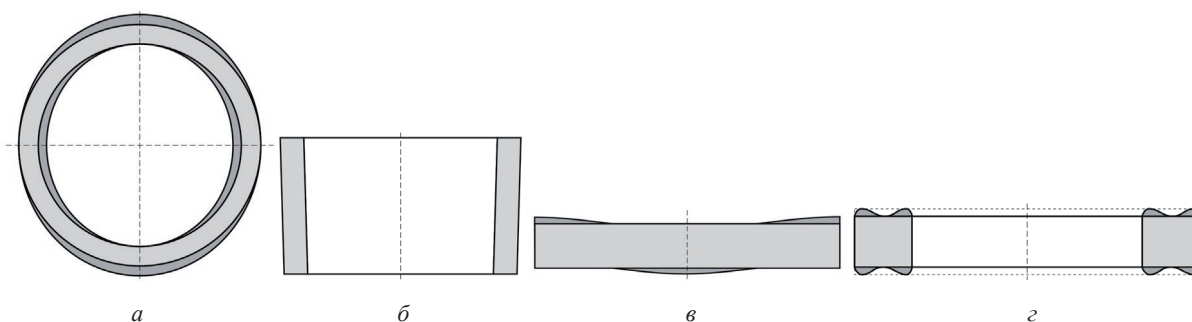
Типичные погрешности кольцевых заготовок после кольцераскатки:
